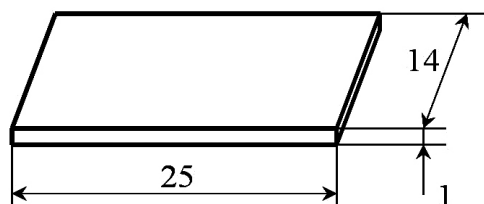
Чертеж образца для испытания на газоабразивный износ
